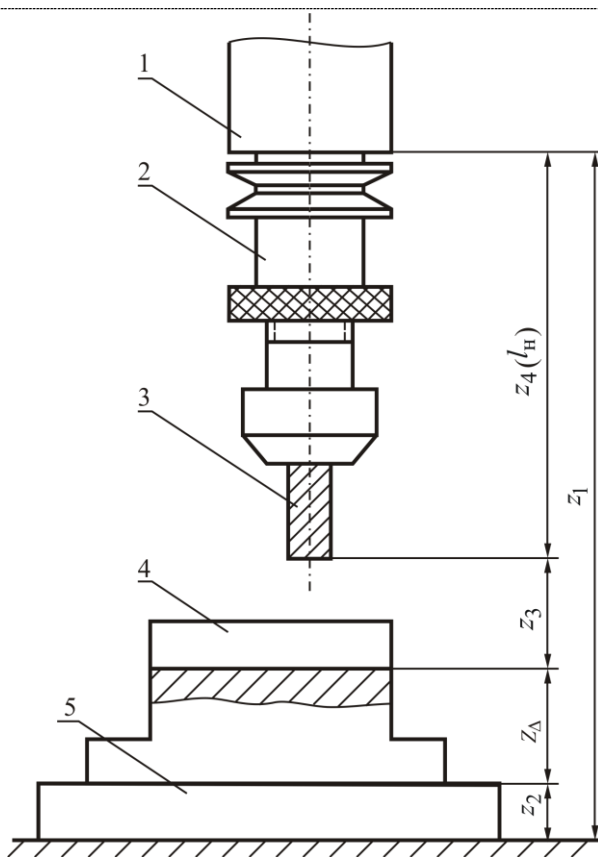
Технологическая размерная цепь настройки станка с ЧПУ типа «обрабатывающий центр»: 1 – шпиндель станка; 2 – державка инструментального блока; 3 – фреза; 4 – деталь; 5 – приспособление
